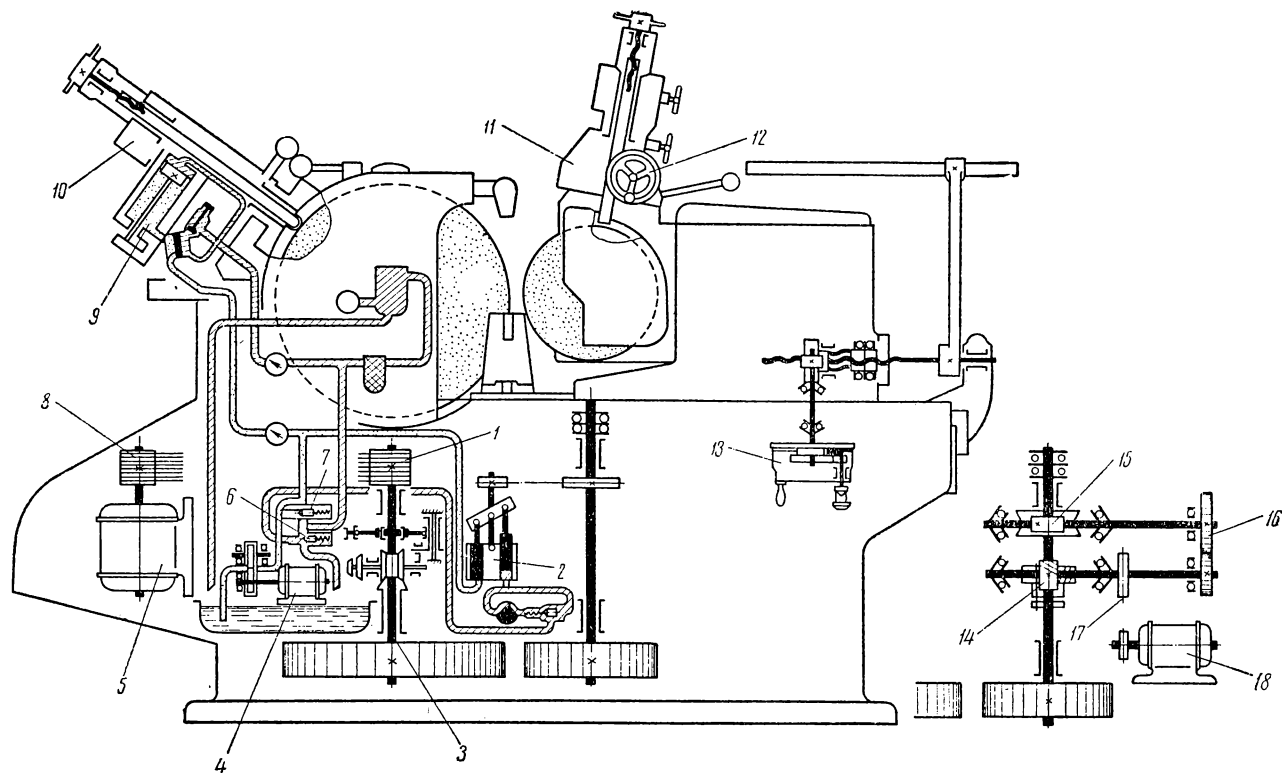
Кинематическая схема бесцентровошлифовального станка 3180
